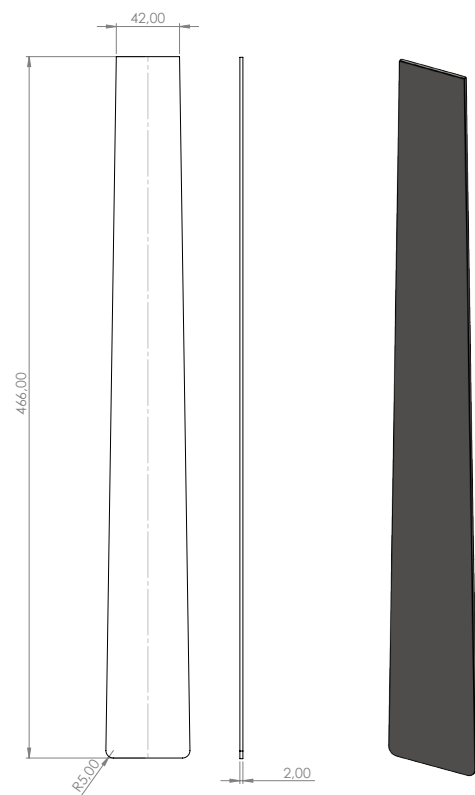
Desenho técnico e modelo 3D - *Fretboard* de aço para maquete.
